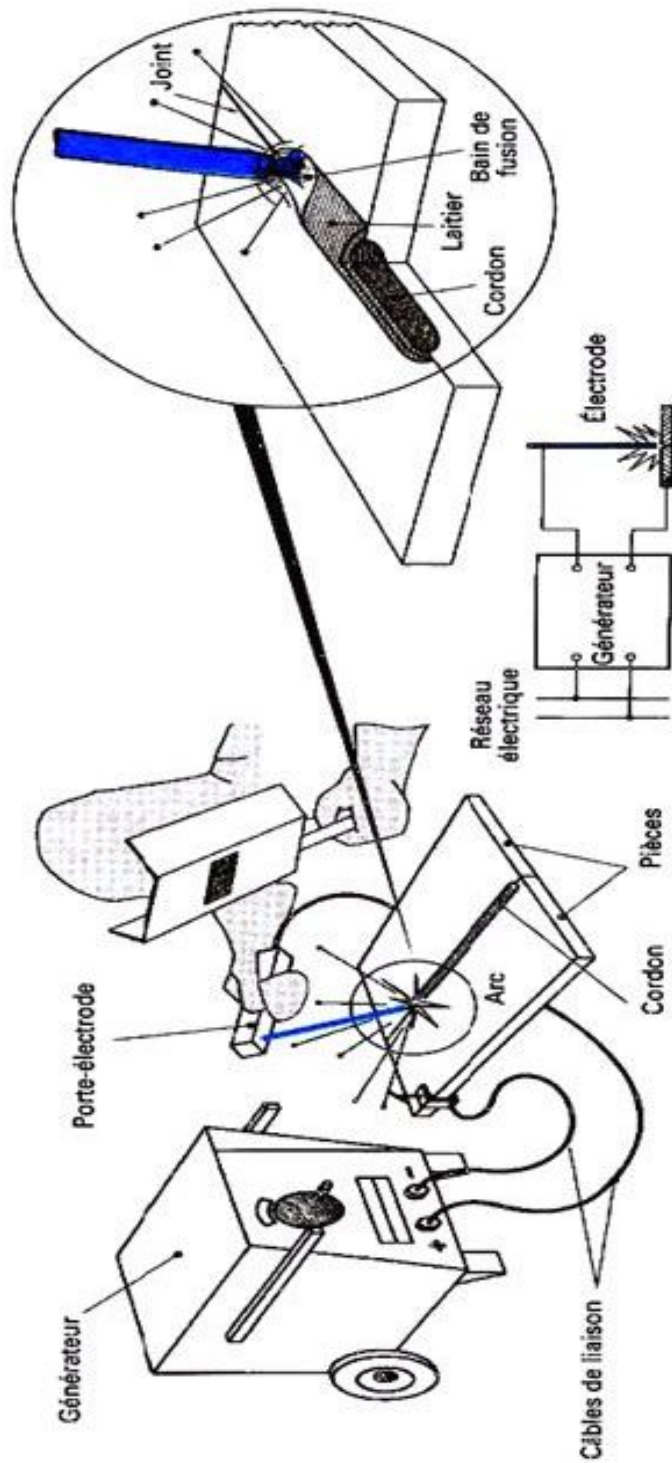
Principe du soudage à l'électrode enrobée.
